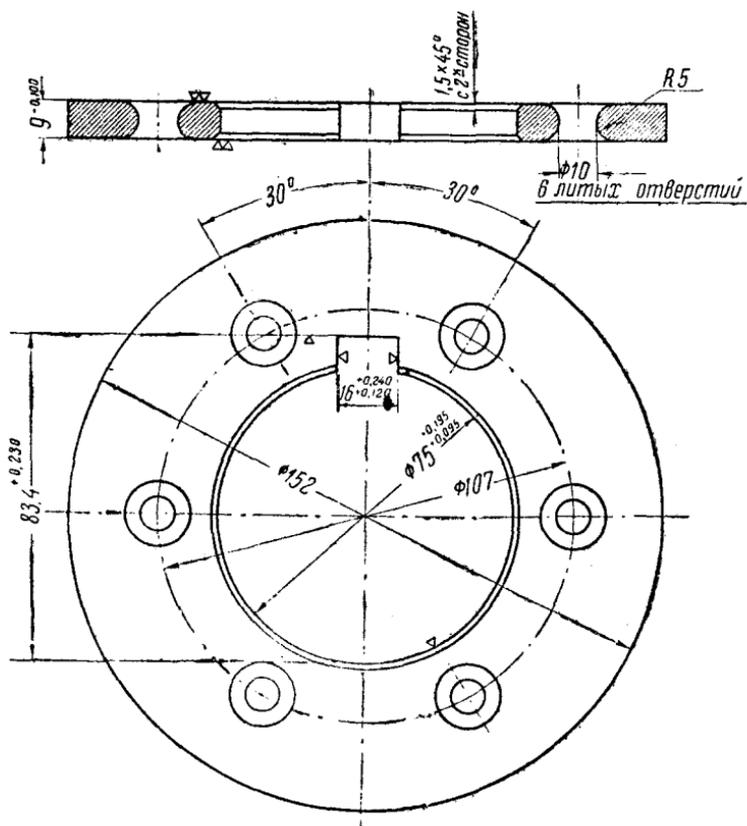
Дет. № 03113. Диск коленчатого вала упорный
